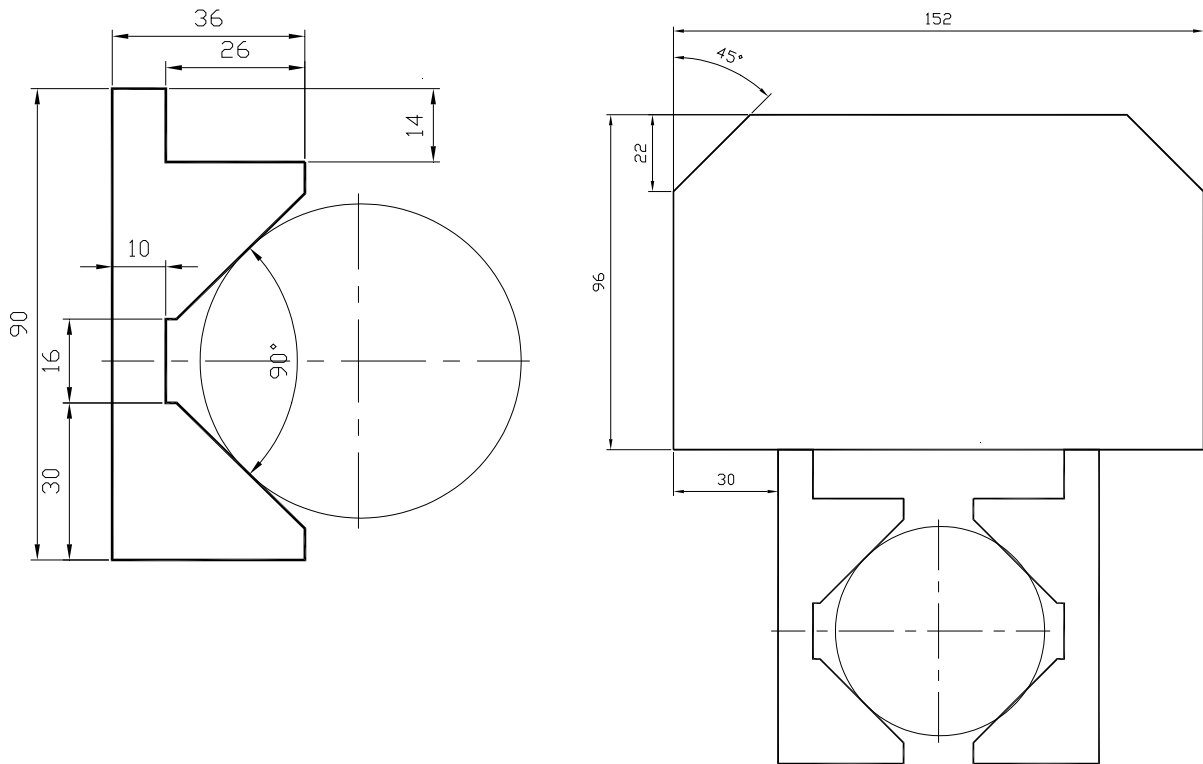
Контур поперечного сечения левого призматического рычага схвата и корпуса схвата
